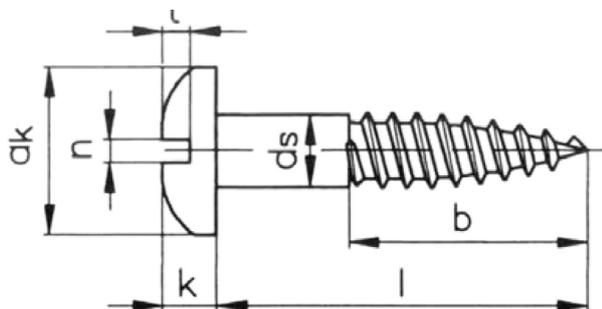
| Tornillo DIN96 | Fuente: DISLA
